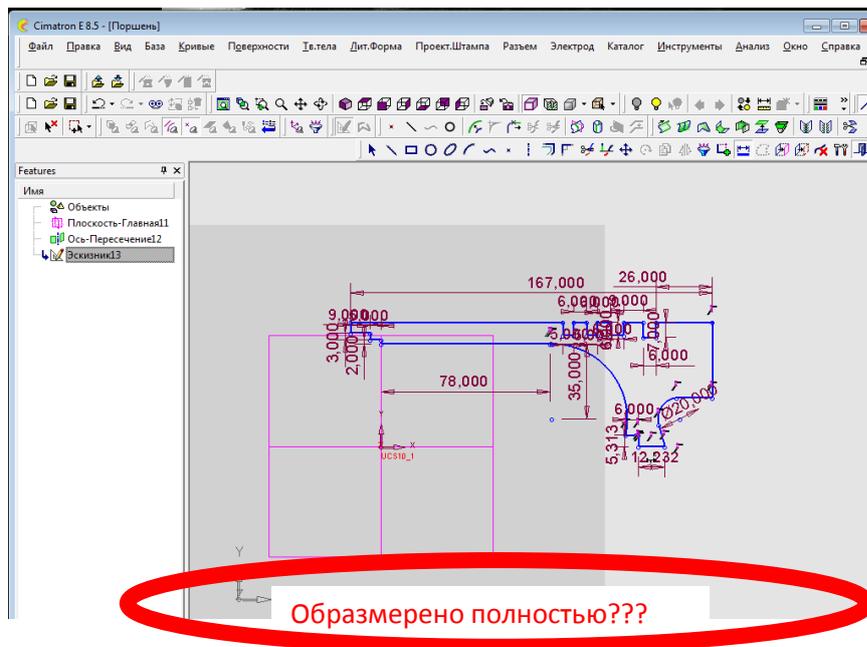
Образмеренный эскиз (Поршень.elt)
